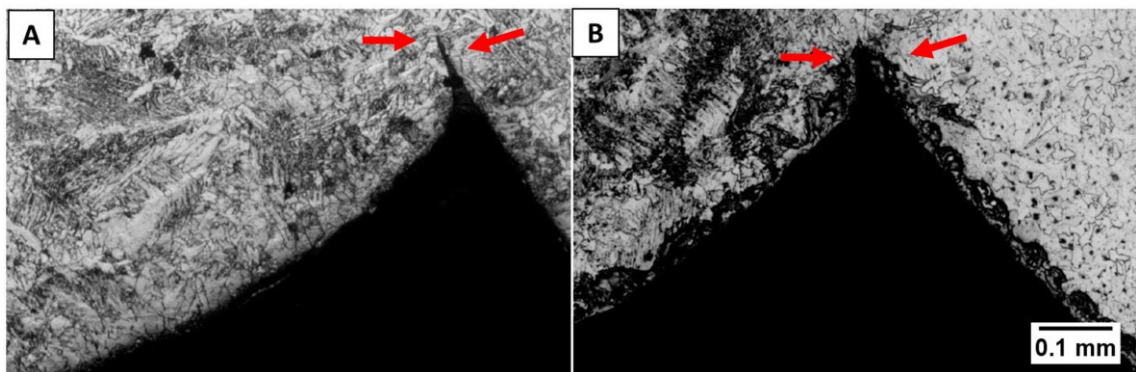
Detalhe nas regiões de descontinuidade soldagem GMAW. a) Condição de soldagem 2. b) Condição de soldagem 6. (Próprio autor)
